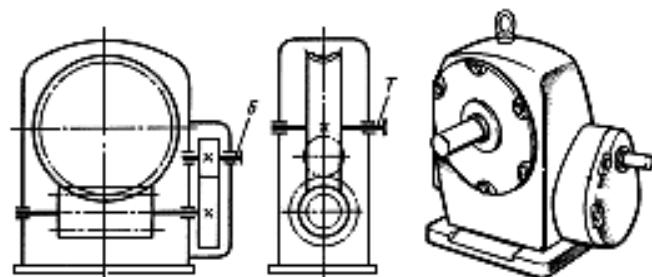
Червячно-цилиндрический двухступенчатый редуктор
